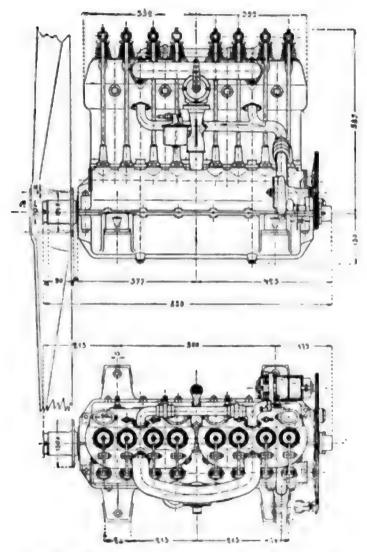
u. Fig. 276. Seitenansicht und Draufsicht.
